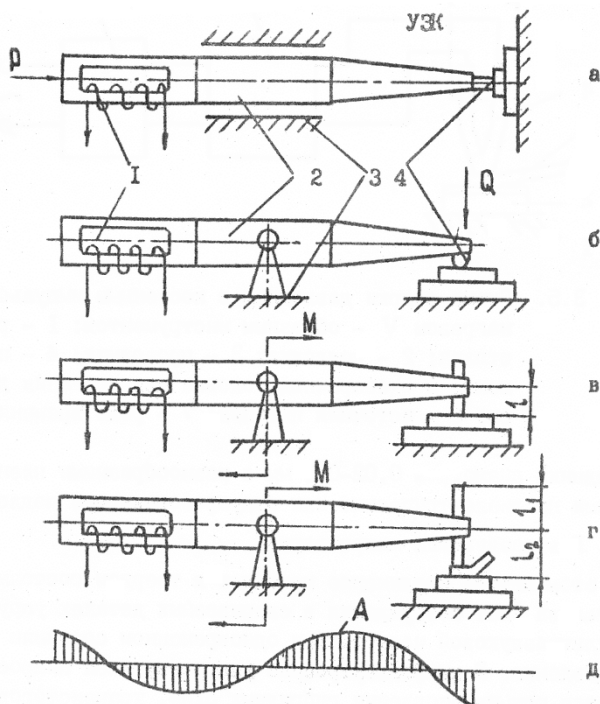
Ультразвуковые колебательные системы для микро-сварки: 1 – преобразователь; 2 – волновод-концентратор; 3 – акустическая развязка; 4 – сварочный инструмент. А – амплитуда колебаний; Р – усилие сжатия; М – момент силы
